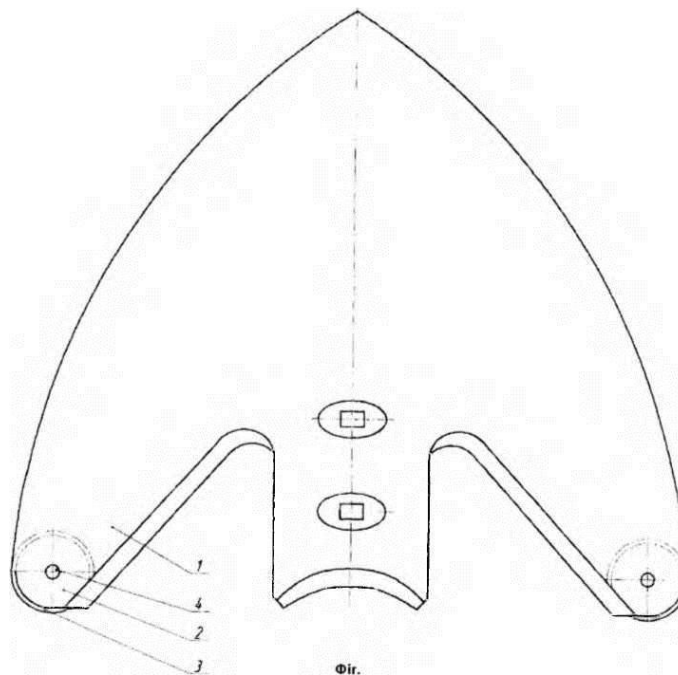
Робочий орган культиватора [8], вид зверху
